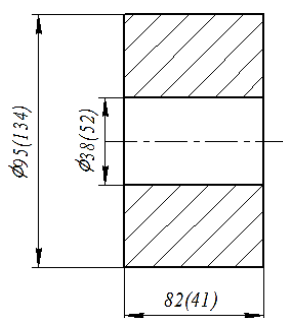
Эскиз заготовки кольцевой формы для пластической осадки
